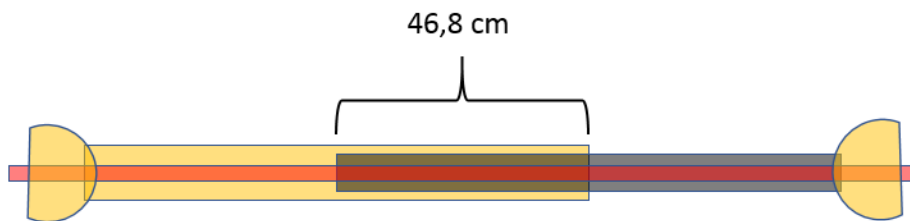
Croquis du chevauchement des sections d'un protecteur en bon état (Source : CNESST)
